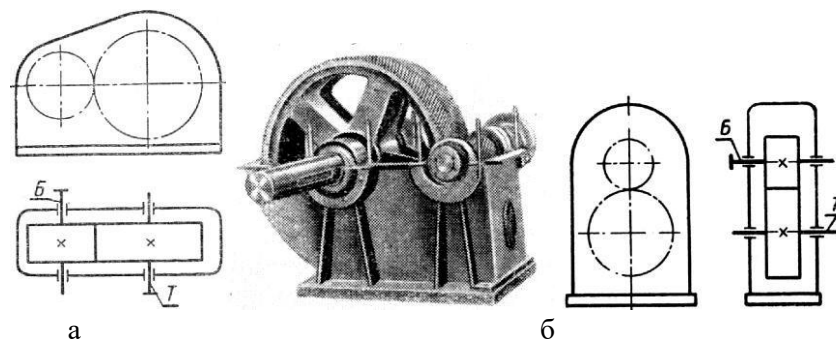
Одноступінчаті редуктори з циліндричними зубчастими колесами
